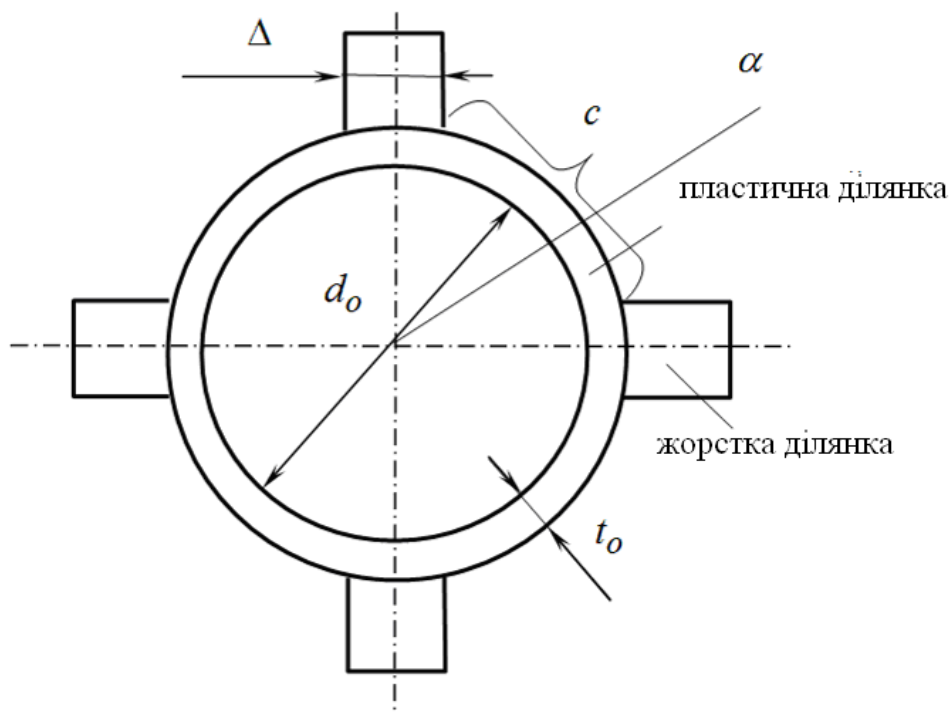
Схема деформування заготовки із жорсткими та пластичними ділянками
